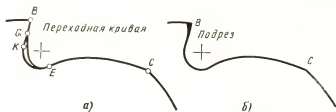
Переходные кривые и подрезы на профиле зубьев цилиндрической фрезы
